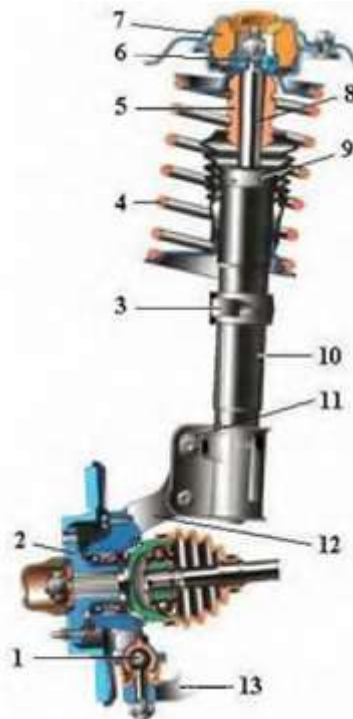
Конструкція підвіски Макферсон (фрагмент):
